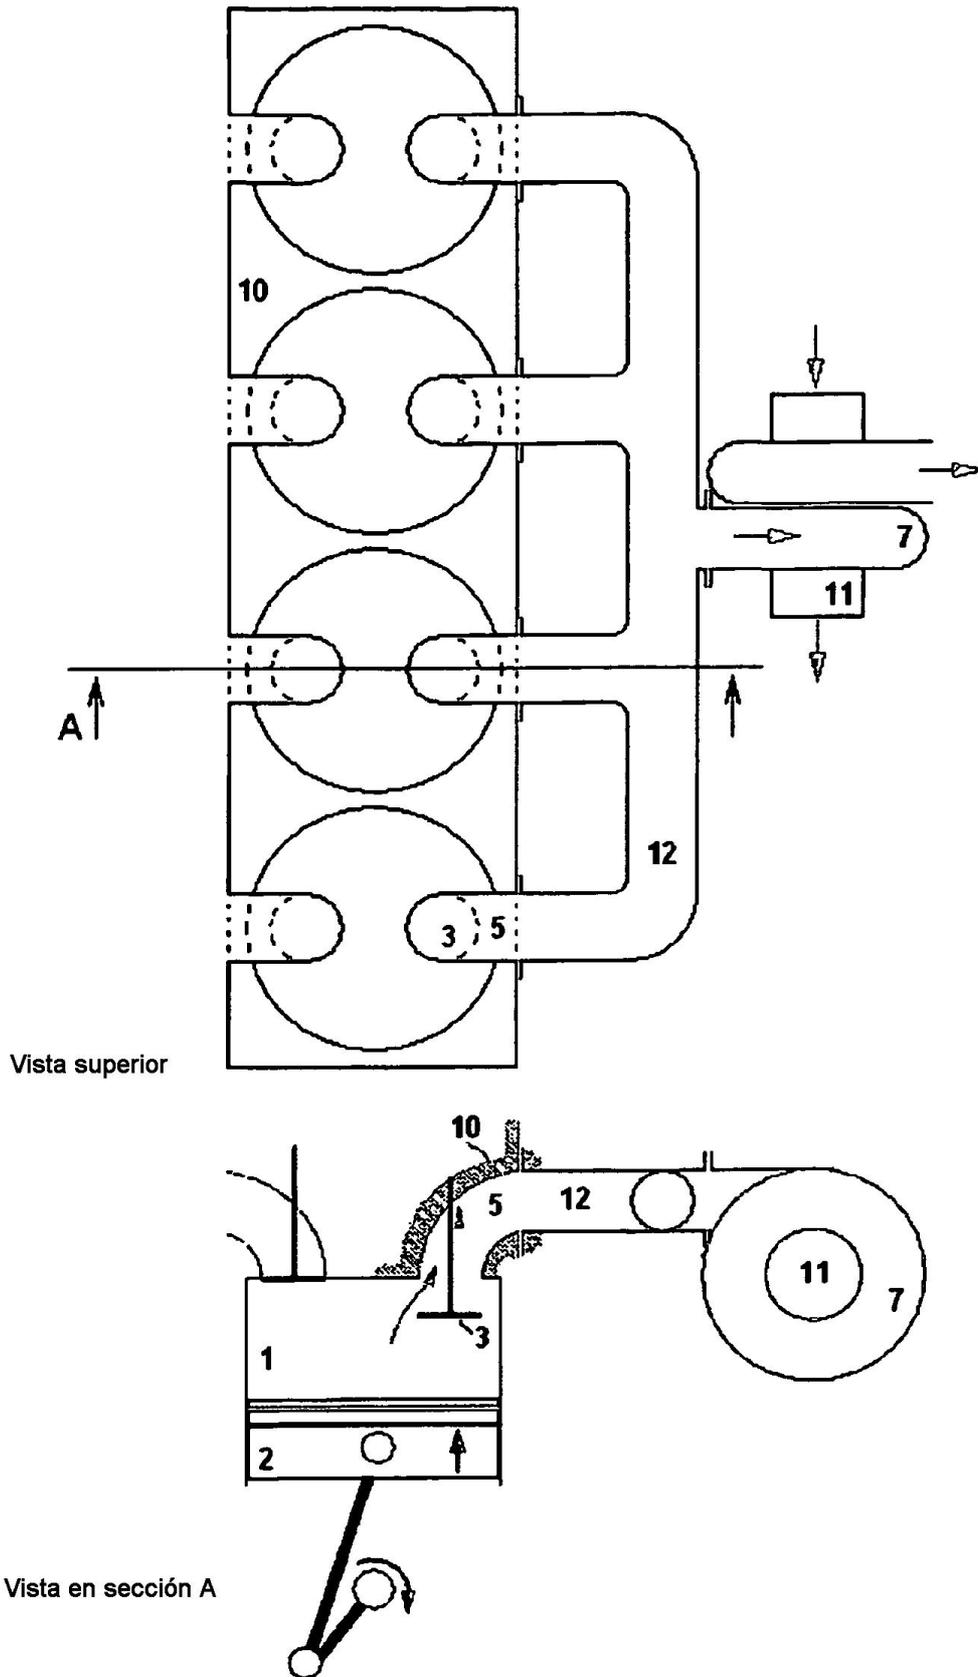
Turbina montada en un motor, según el estado de la técnica, con colector de escape (12)
